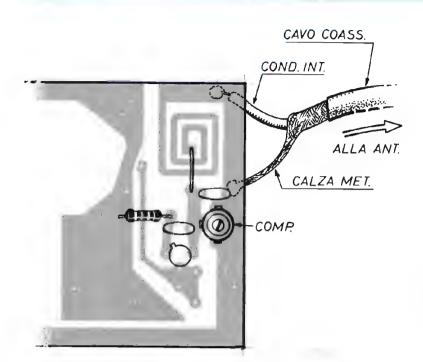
Servendosi di un dipolo per FM, il cavo coassiale di discesa deve essere collegato al circuito stampato del microtrasmettitore nel modo indicato in questo disegno.
